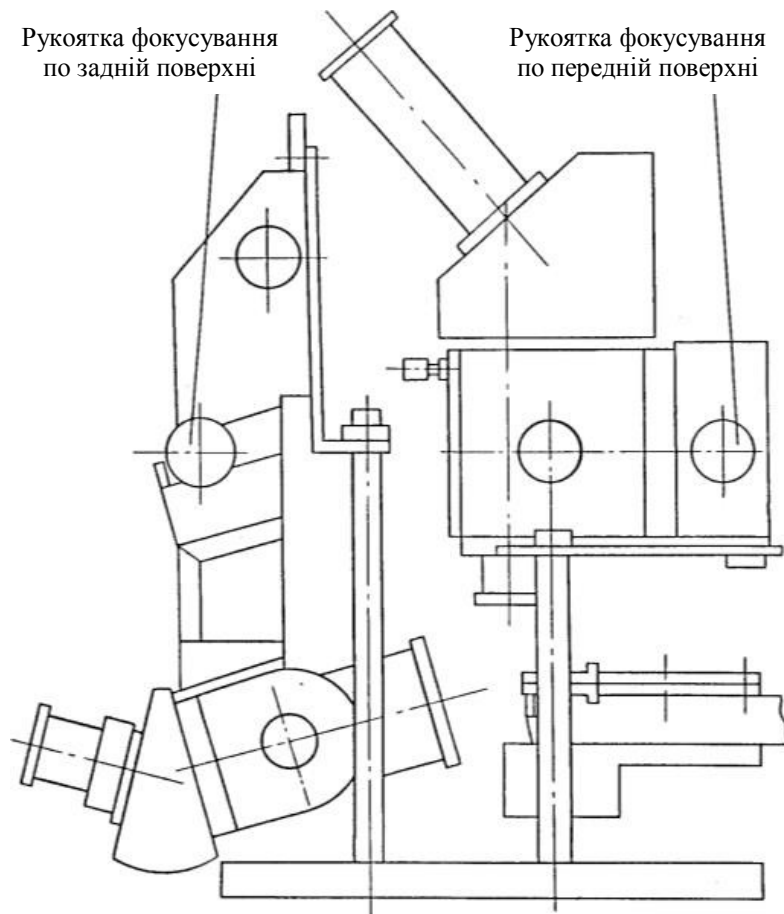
Вимірювальний пристрій МБС-9
